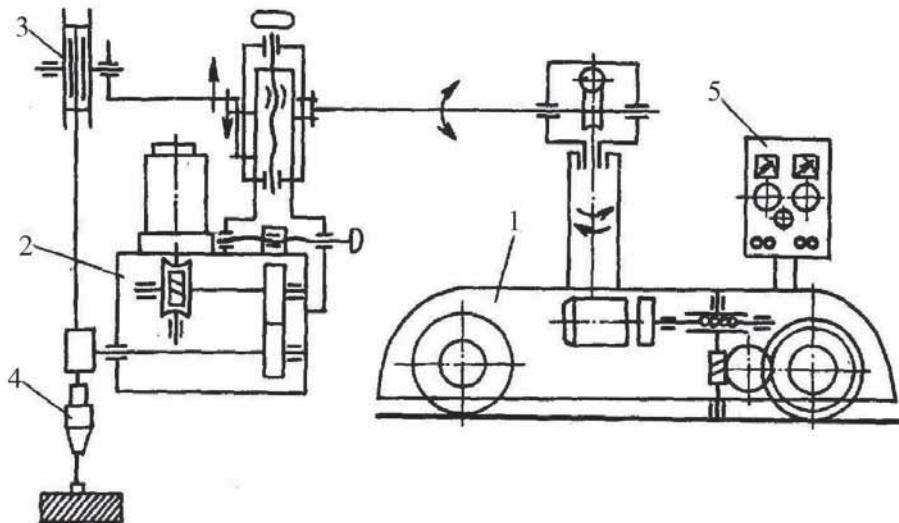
Схема для сварки плавящимся электродом: 1 – тележка; 2 – подающий механизм; 3 – кассета с электродной проволокой; 4 – горелка; 5 – пульт управления
